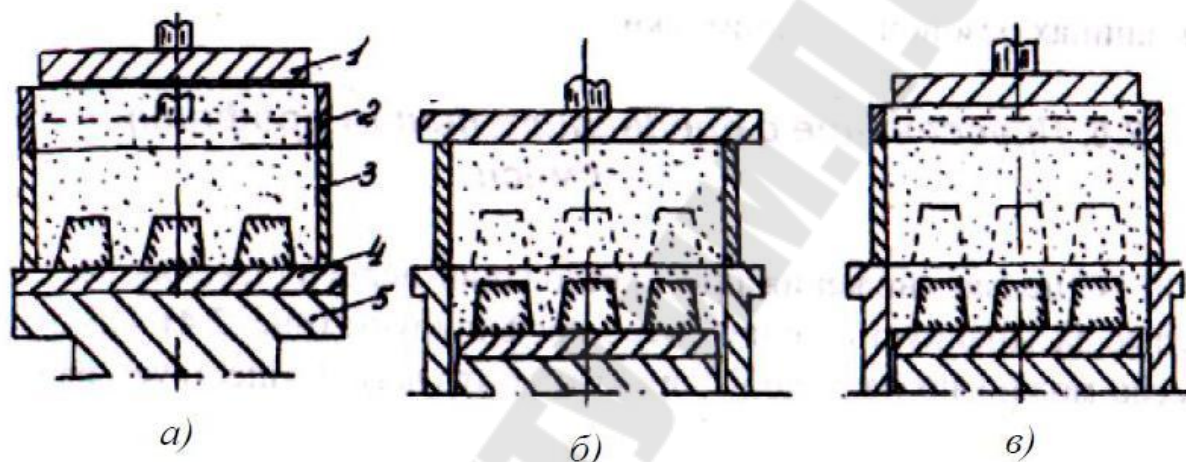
Способы прессования: а- верхнее; б- нижнее; в- двухстороннее; 1- прессовая колодка; 2- наполнительная рамка; 3-опока; 4- модельная плита; 5- стол
